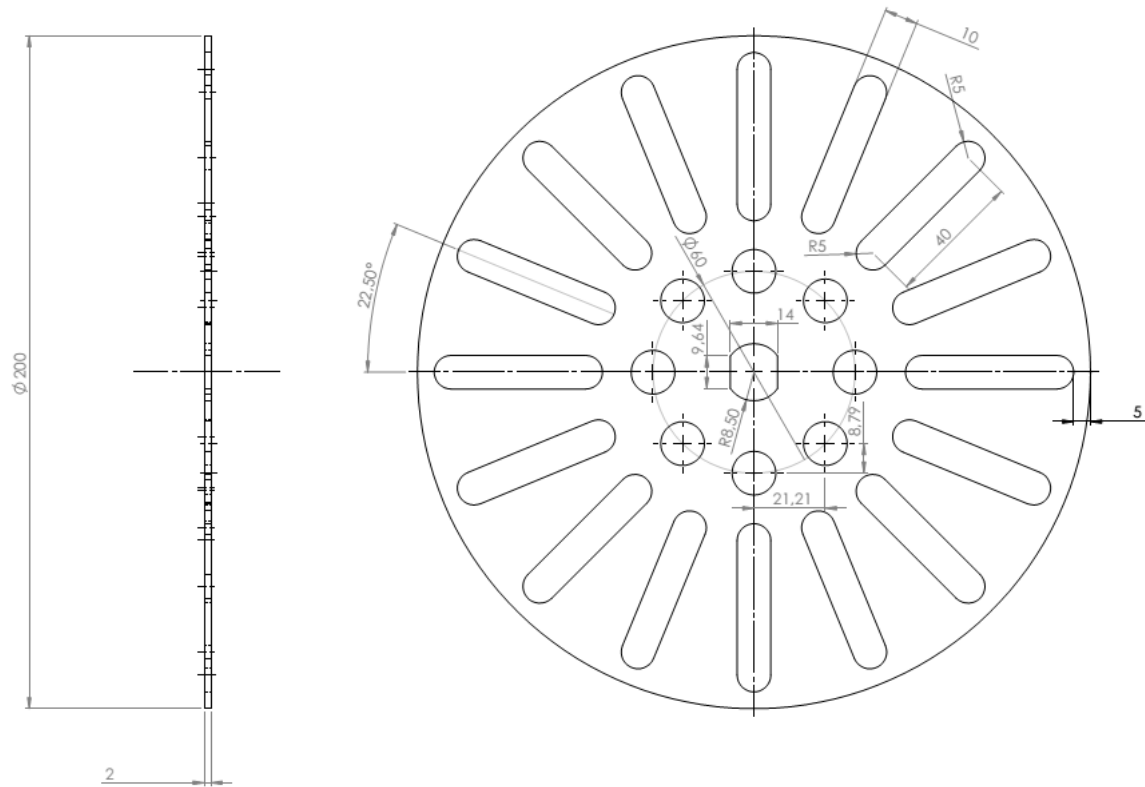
Dimensões (em milímetros) dos discos do rotor tipo C.
